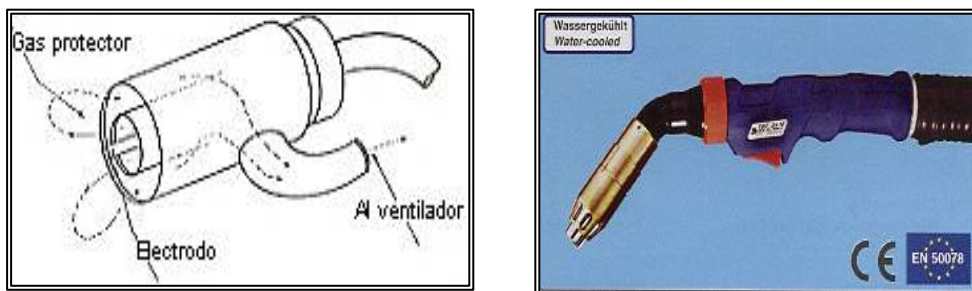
Extracción incorporada a la pistola de soldadura
